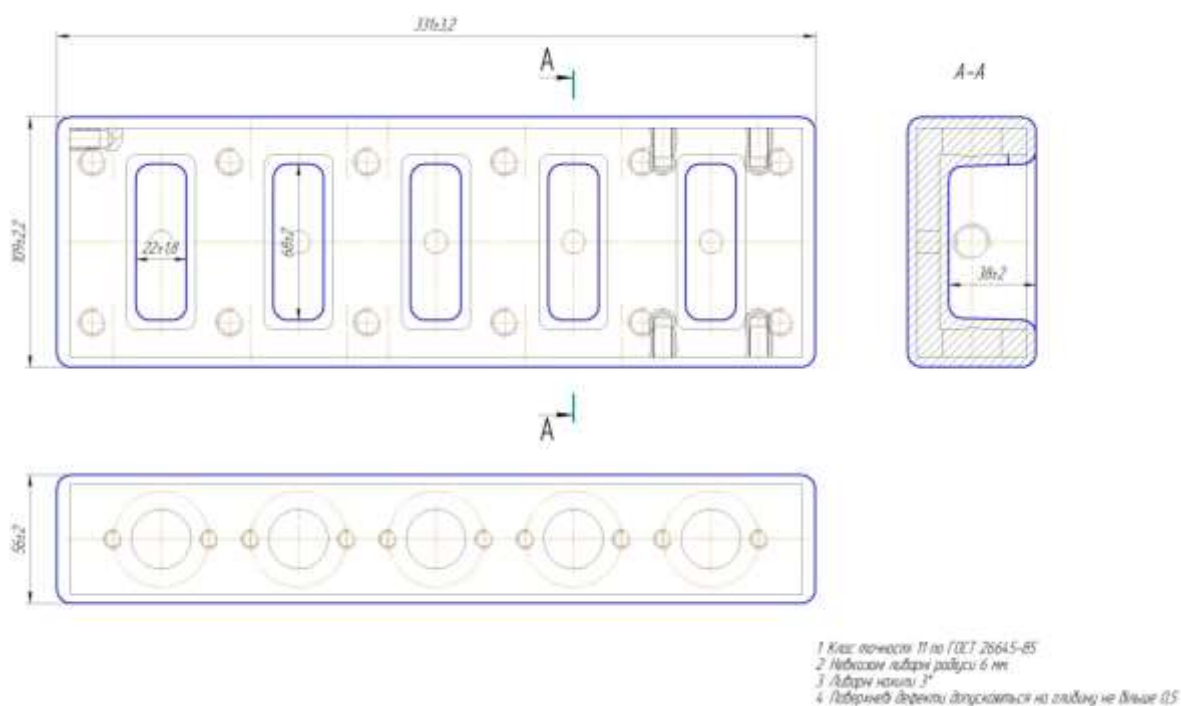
Кресленик заготовки деталі «Корпус»
